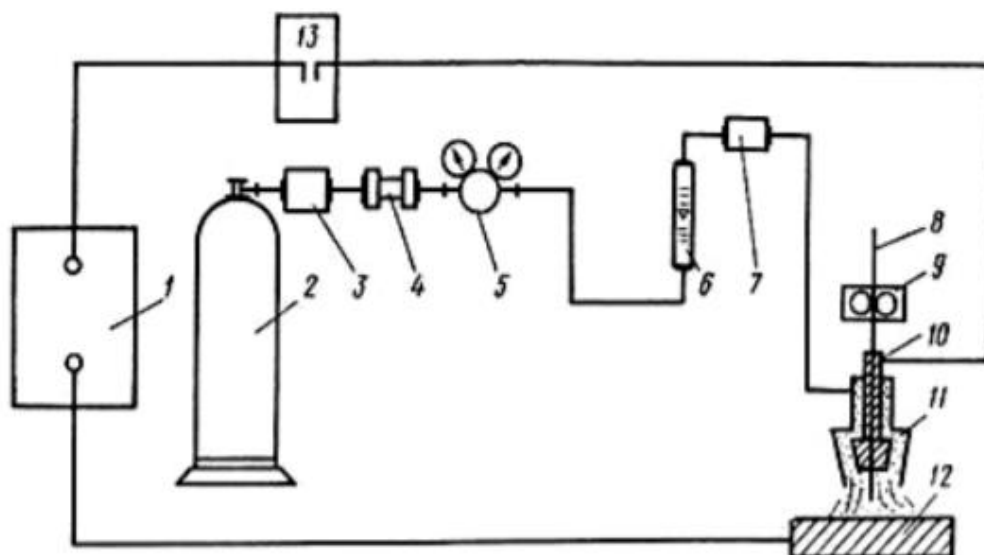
Схема установки для наплавлення в середовищі CO_2 :
